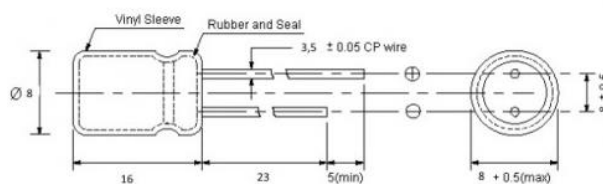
Габаритні розміри конденсатора типу b41828 "Epcos"
